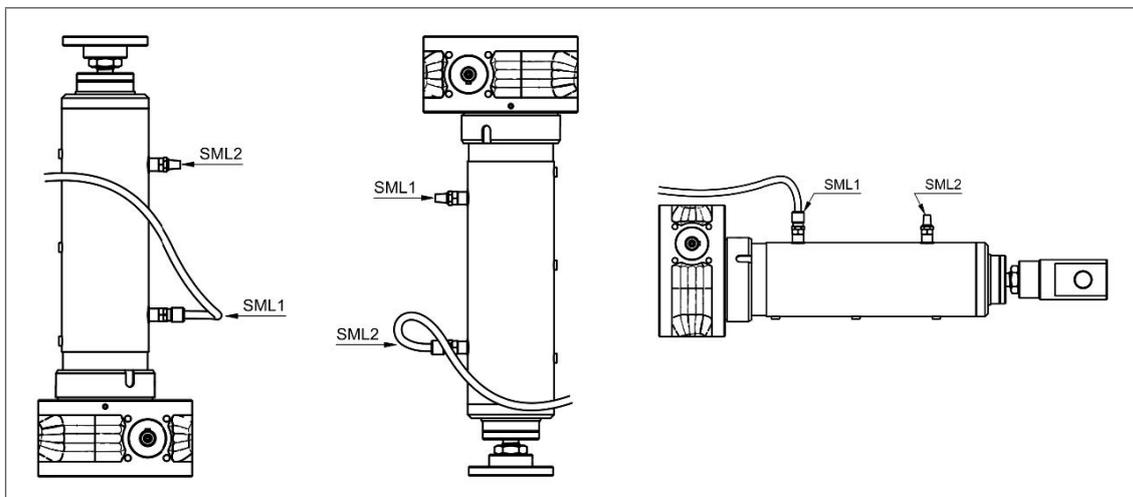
Posizione di ventilazione con lubrificazione automatica
